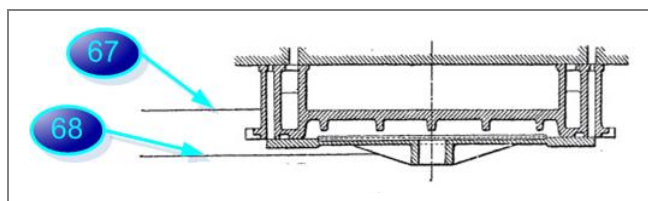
1900 – MACHINE A VAPEUR FIGUET - SCHEMA DES DEUX TIROIRS SUPERPOSES
